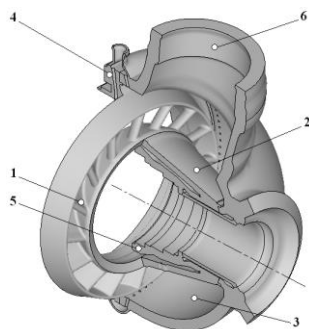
Статор турбины (в разрезе): 1 – лопатки соплового аппарата; 2 – конус; 3 – сфера; 4 – фланец статора; 5 – фланец опоры подшипника; 6 – входной патрубок
